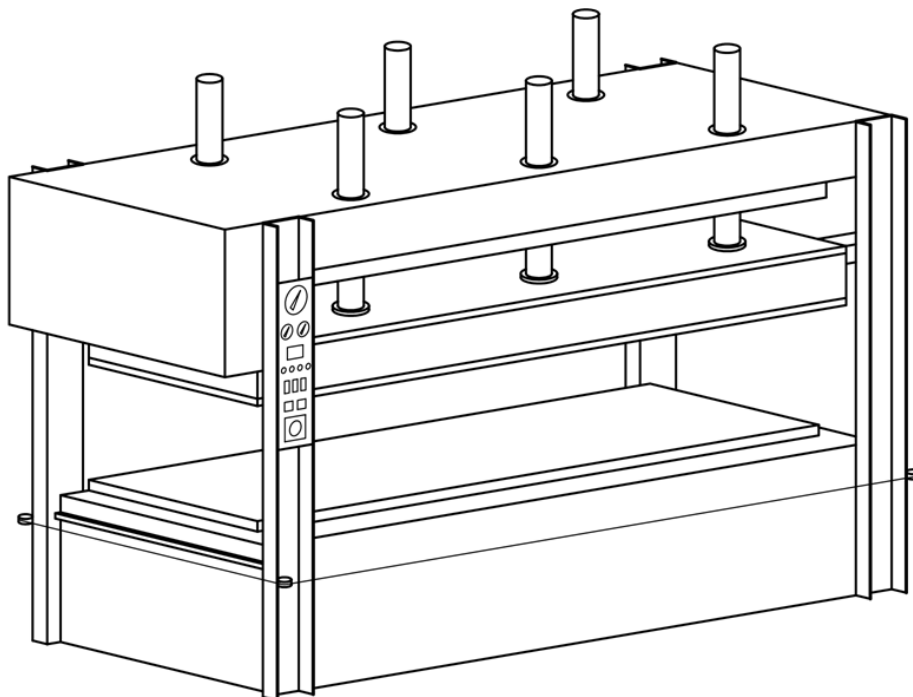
Пример прессы холодного или горячего прессования с верхними приводами
